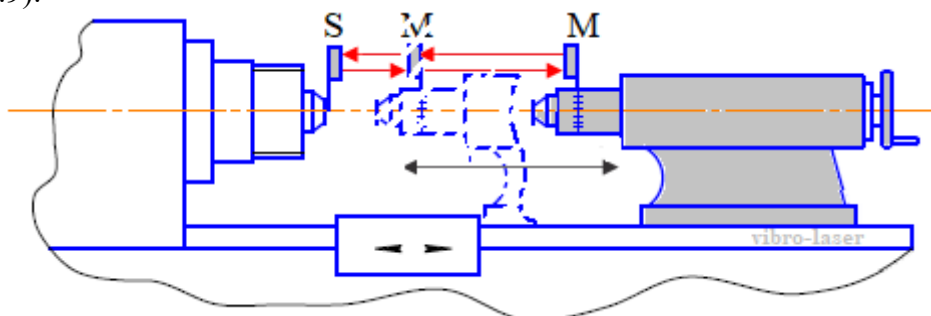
Установка лазерных головок S и M системы лазерной центровки
